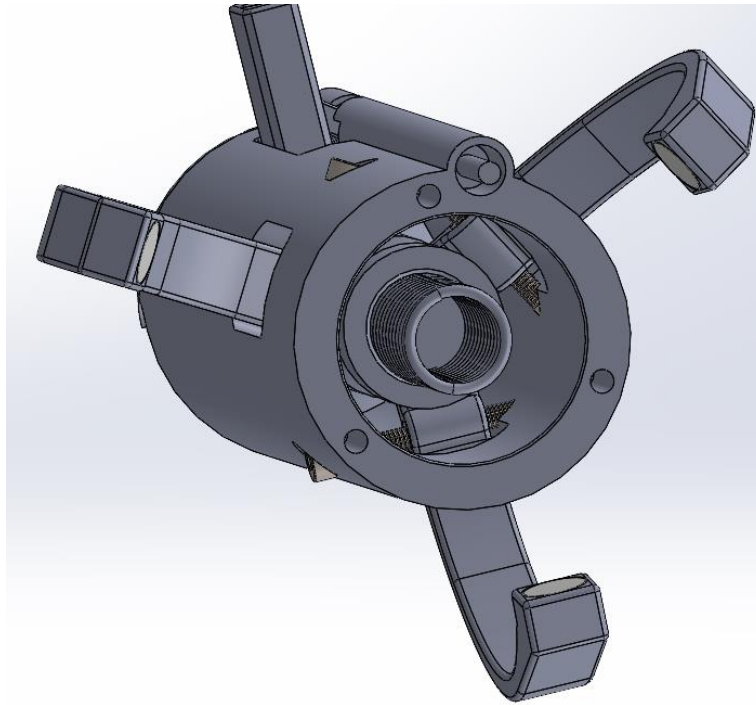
Treceava imagen de montaje, posición del Muelle 1.
